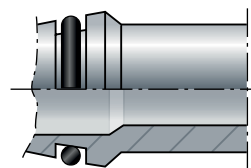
Dichtkegel 24° mit O-Ring: Form B für Schlauchanschluss
